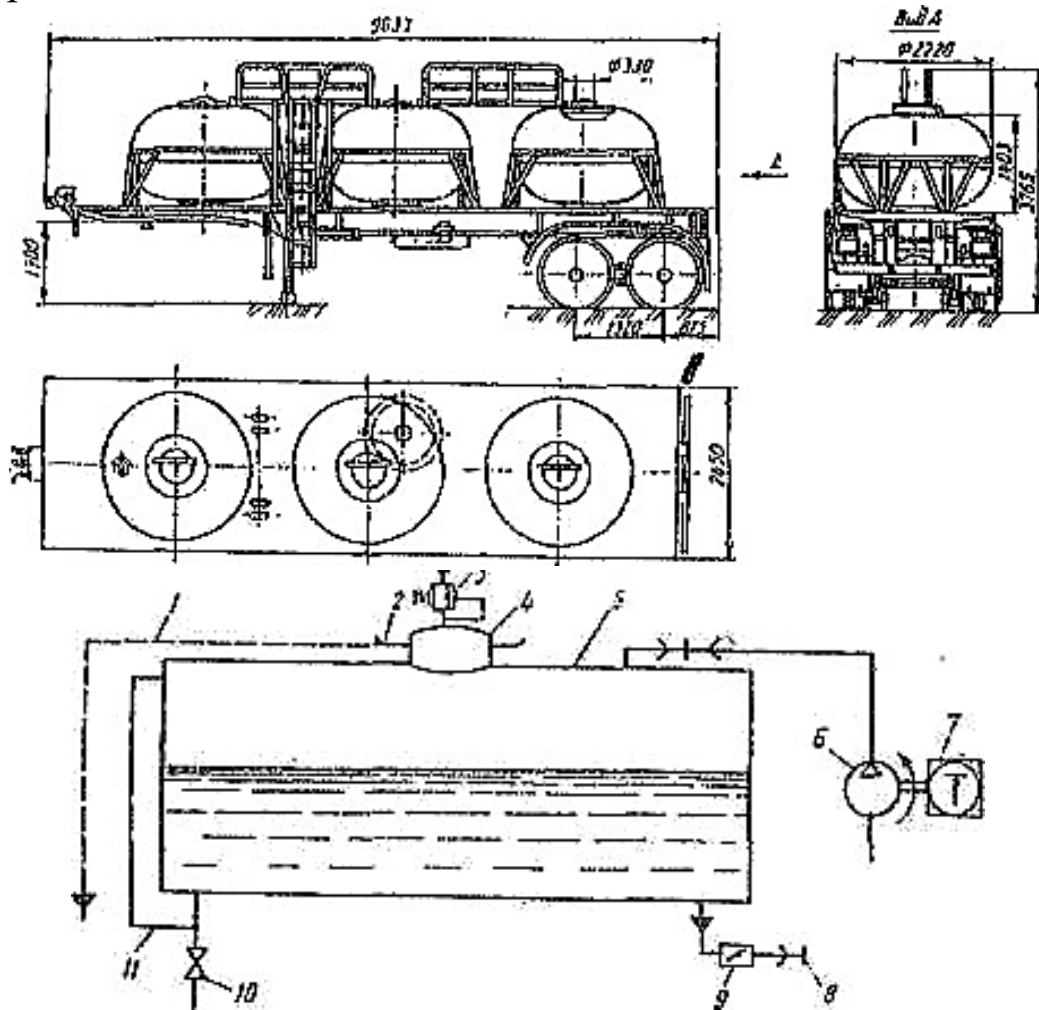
Принципиальная схема технологического оборудования полуприцепа-цистерны ЕД-20,5-1 с мотокомпрессором: 1 – сливная трубка; 2 – корытце; 3 – клапан; 4 – люк; 5 – цистерна; 6 – компрессор; 7 – двигатель внутреннего сгорания; 8 – быстросъемная муфта; 9 – затвор; 10 – кран; 11 – уровнемер
